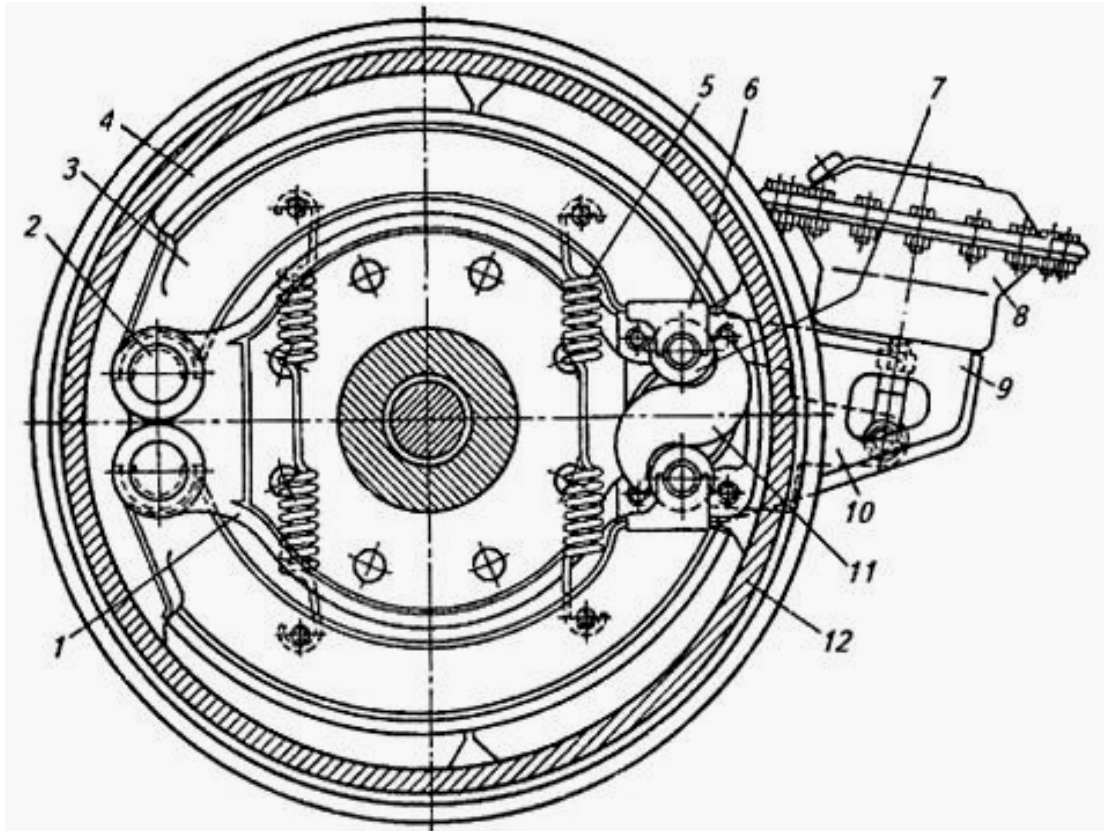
Барабанный тормозной механизм: 1 - суппорт; 2 - опора колодки; 3 - колодка; 4 - фрикционная накладка; 5 - оттяжная пружина; 6 - опора ролика; 7 - ролик; 8 - тормозная камера; 9 - кронштейн тормозной камеры; 10 - регулировочный рычаг; 11 - разжимной кулак; 12 - тормозной барабан
